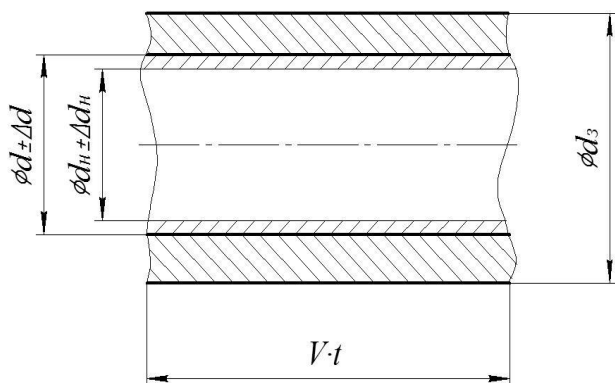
Схема наплавленої циліндричної трубчастої заготовки
